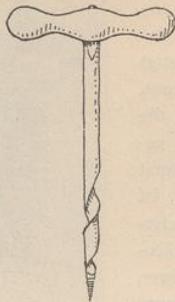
Bohrer. Nagelbohrer mit einem Querheft zum Umdrehen des Bohrers.
